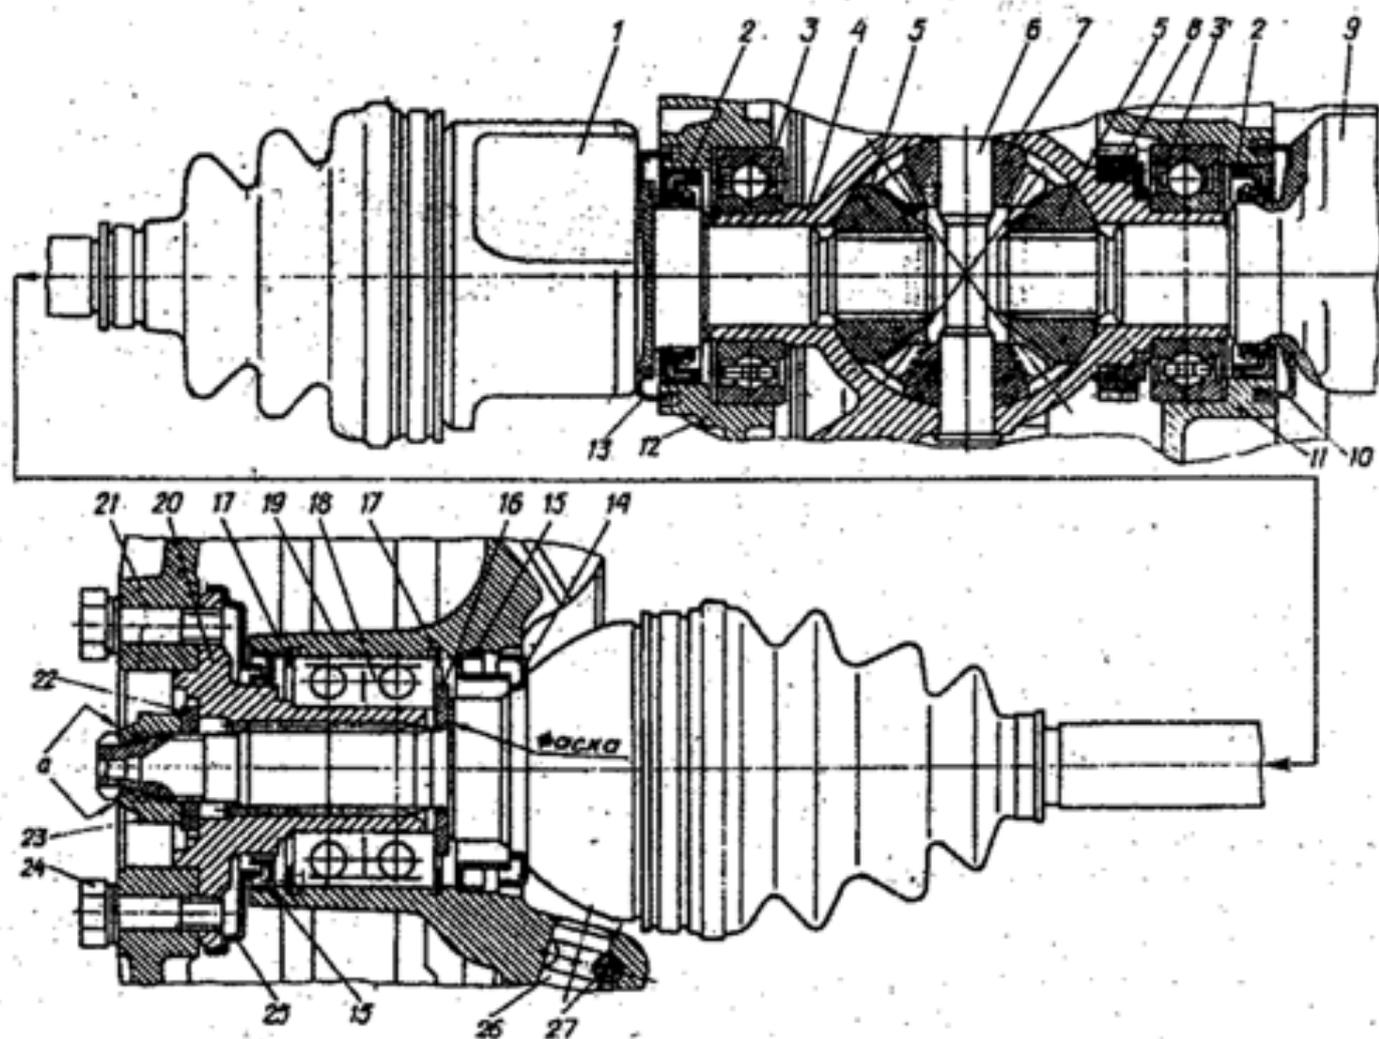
Шарниры привода колес, дифференциал и ступица: 1 - шарнирный вал левый в сборе; 2 - манжета; 3 - подшипник; 4 - коробка дифференциала; 5 - шестерня полуоси; 6 - ось сателлитов; 7 - сателлит; 8 - шестерня ведущая спидометра; 9 - шарнирный вал правый в сборе; 10 - грязеотражатель внутренний; 11 - картер сцепления; 12 - картер коробки передач; 13 - грязеотражатель внутренний; 14 - грязеотражатель наружный; 15 - грязеотражатель поворотного кулака; 16 - шайба промежуточная; 17 - кольцо стопорное подшипника; 18 - подшипник ступицы; 19 - кулак поворотный; 20 - ступица; 21 - фланец ступицы; 22 - шайба; 23 - гайка ступицы; 24 - болт крепления фланца; 25 - грязеотражатель ступицы; 26 - палец шарового шарнира; 27 - болт крепления шарового пальца (клепмное соединение);
